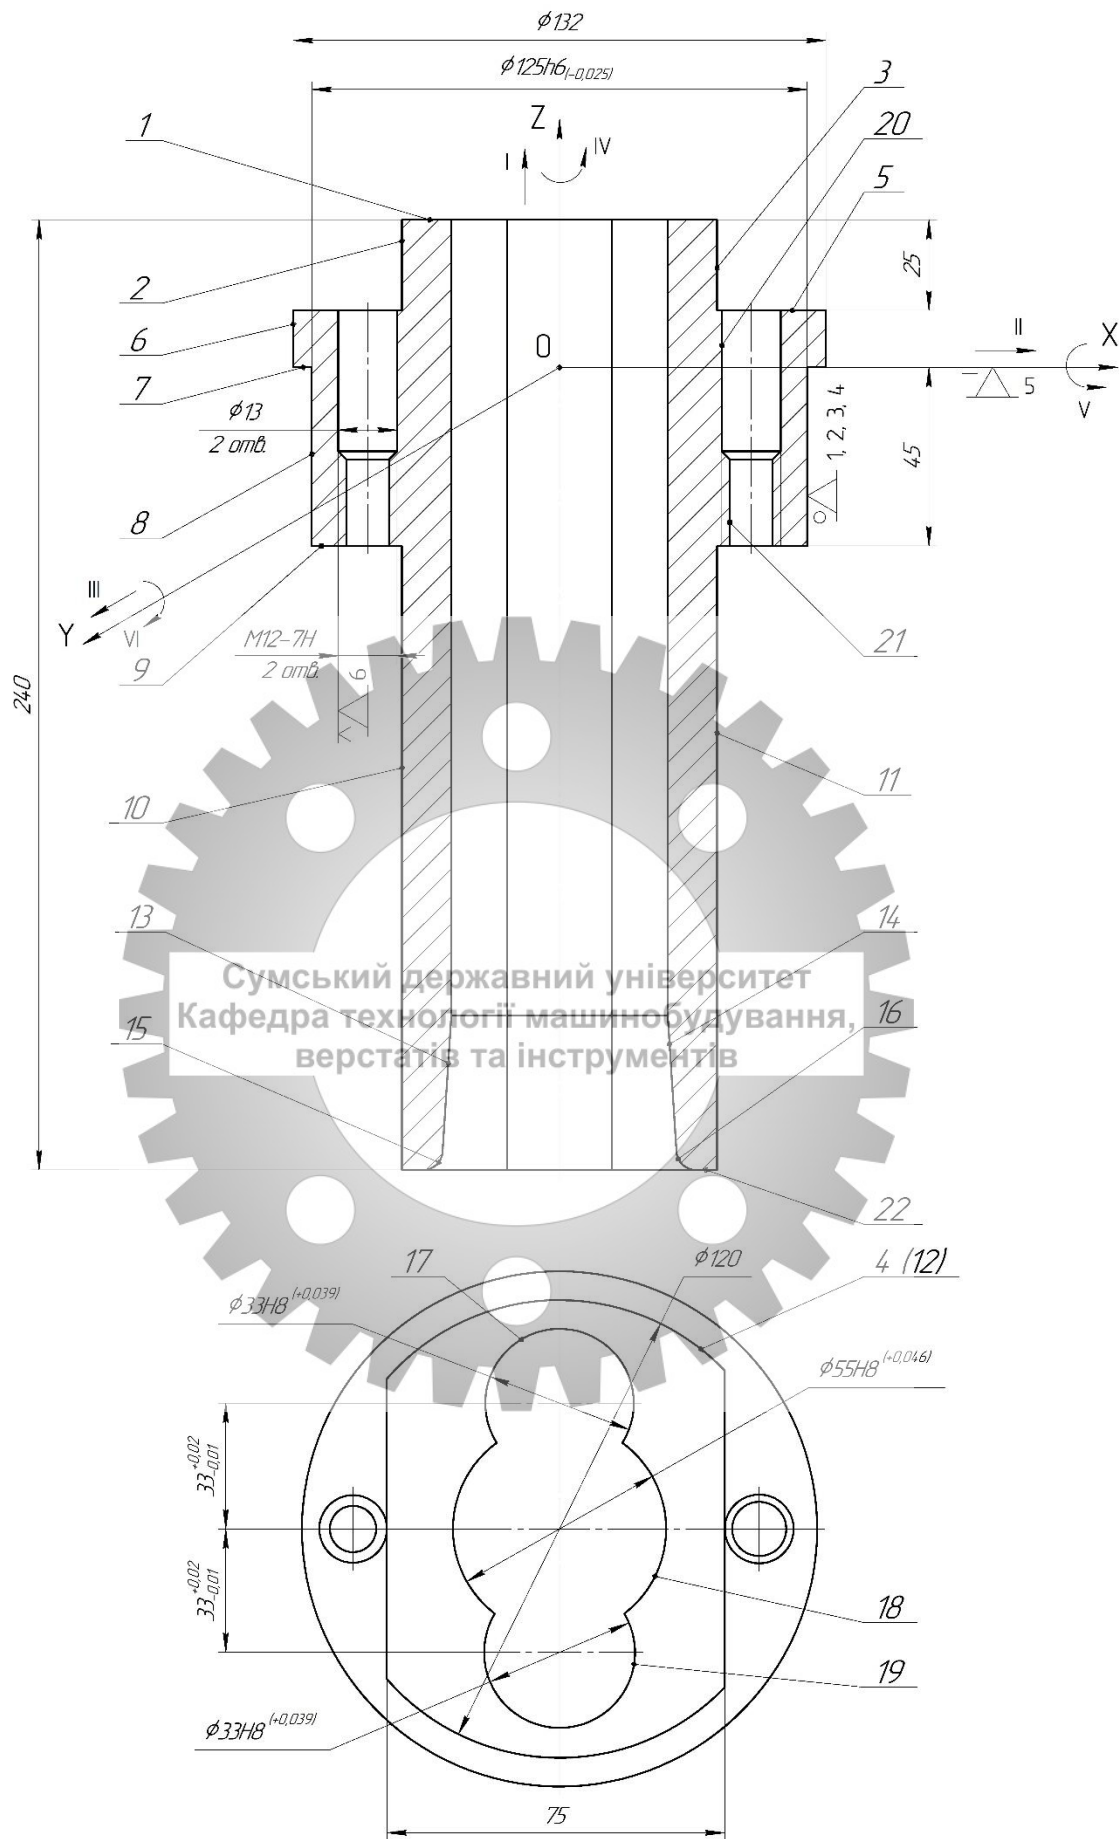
Ескіз деталі із номерами поверхонь
